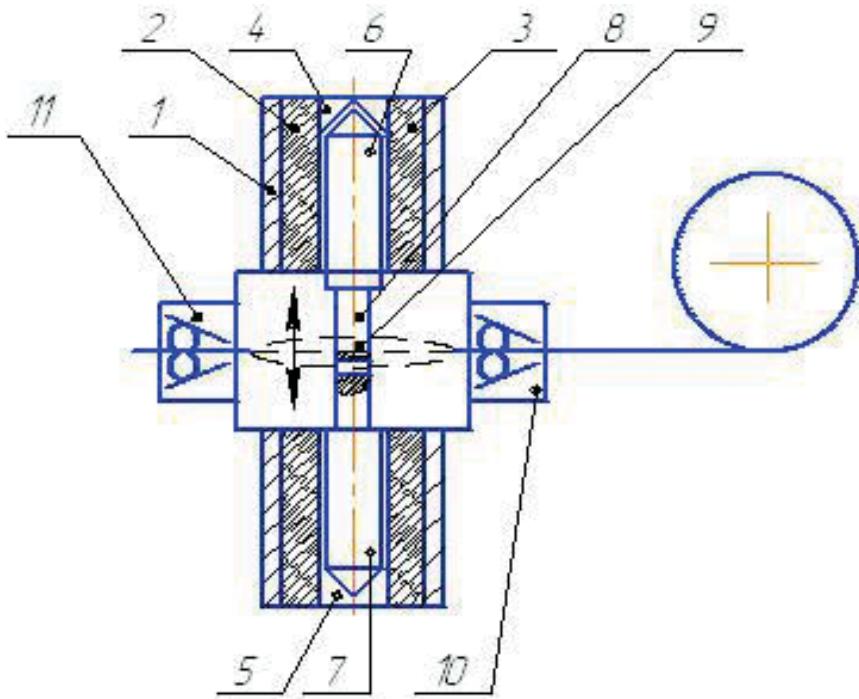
Двухобмоточный электромагнитный механизм с квазиволновым движением сварочной проволоки: 1, 3 – электромагнит; 2 – обмотка; 4, 5 – упор; 6, 7 – сердечник; 8 – втулку; 9 – отверстие; 10, 11 – захват
